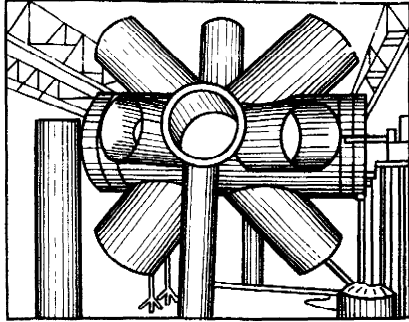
Отдельный сварной узел (ветвь патрубков)
